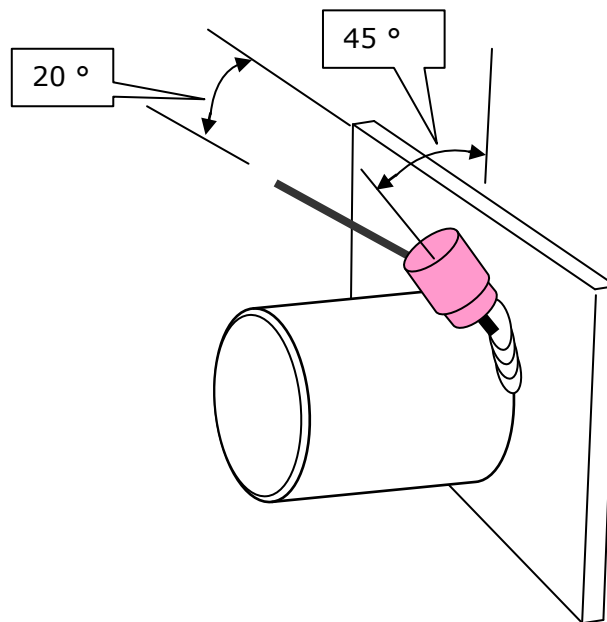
Forma de conducir el porta electrodo y el consumible durante la realización de la soldadura de tubo sobre placa, en posición horizontal.
